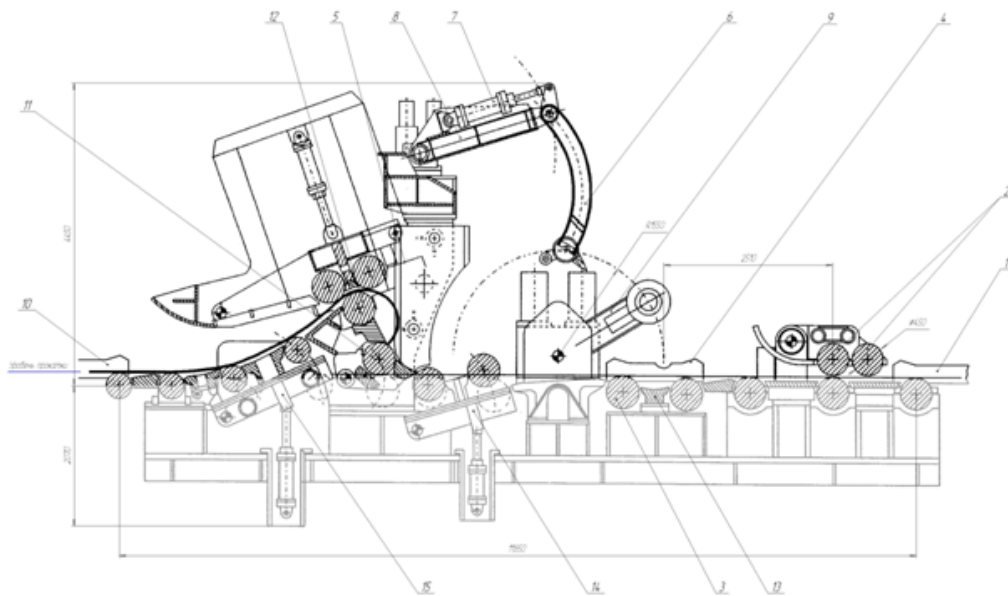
Поперечний переріз типового Койлбокса: 1 – вхідні бічні напрямні Койлбокса; 2 – вхідна ринва; 3 – формуючий рулон ролик; 4 – згинальні ролики; 5 – стабілізатори; 6 – важіль відгибача; 7 – циліндр підгинання; 8 – важіль підгинання; 9 – передатний важіль; 10 – бічні направляючі ножиців; 11 – бічні направляючі роликів колиски № 2; 12 – правильно-тягнучий ролик; 13 – ролики колиски № 1; 14 – ролики колиски № 2
